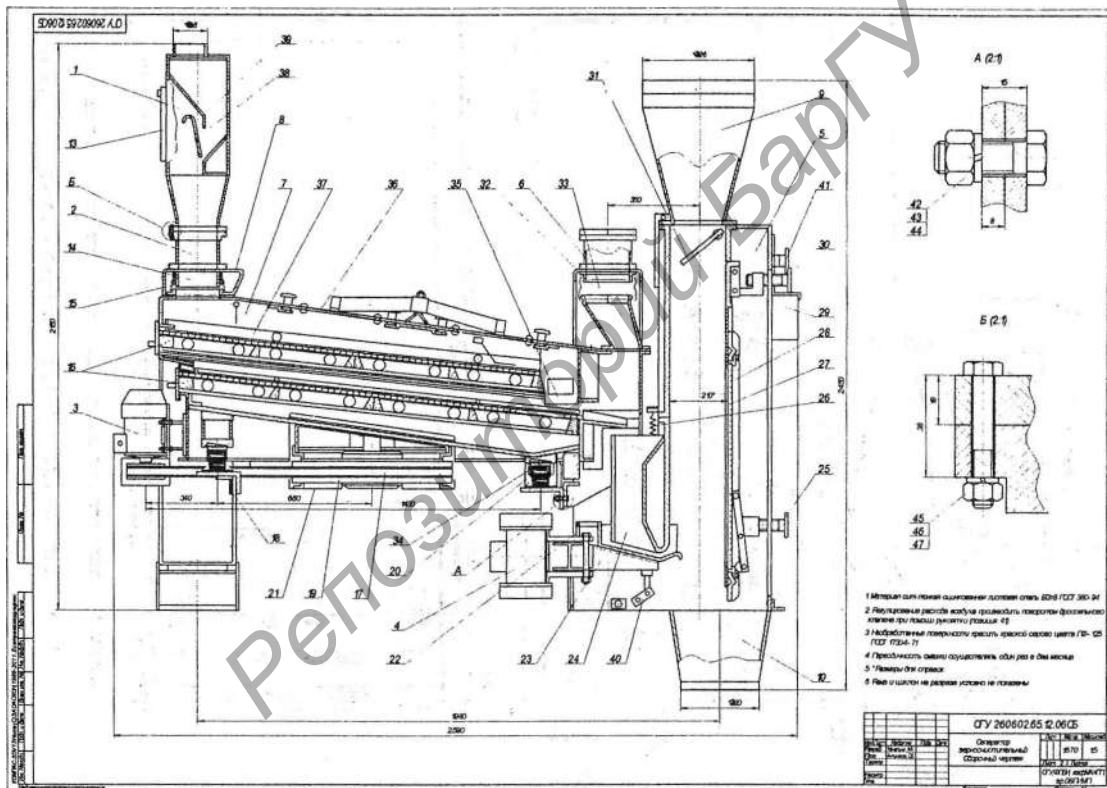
Сборочный чертёж воздушно-решётной машины [42, рис. 33], с изм.
